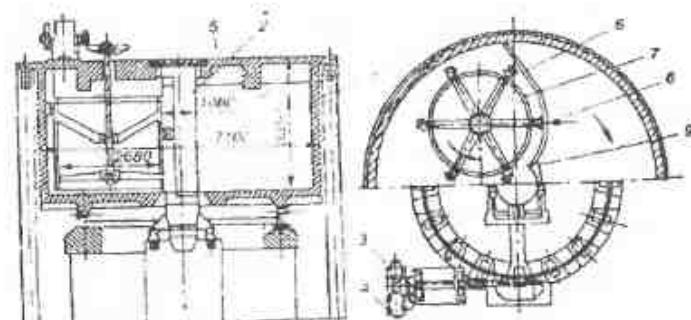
Безперервно діюча суперфосфатна камера: 1—циліндричний корпус камери; 2—центральна труба; 3—електродвигун; 4—редуктор; 5—кришка камери; 6—перегородки; 7—фрезер; 8—отвір для подачі суспензії; 9—екскентрик
